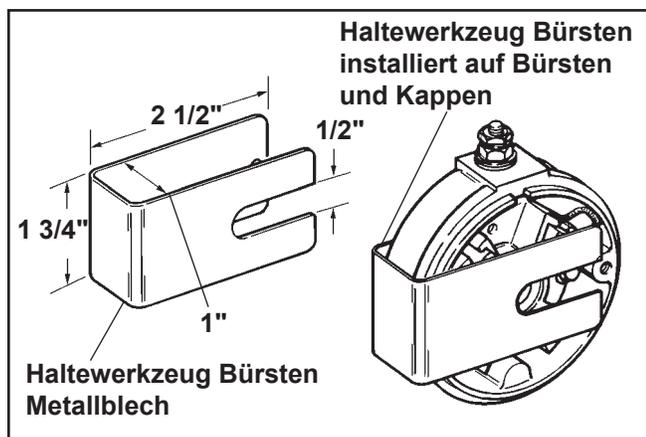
Bürstenhaltewerkzeug (Endkappe Typ "A").
